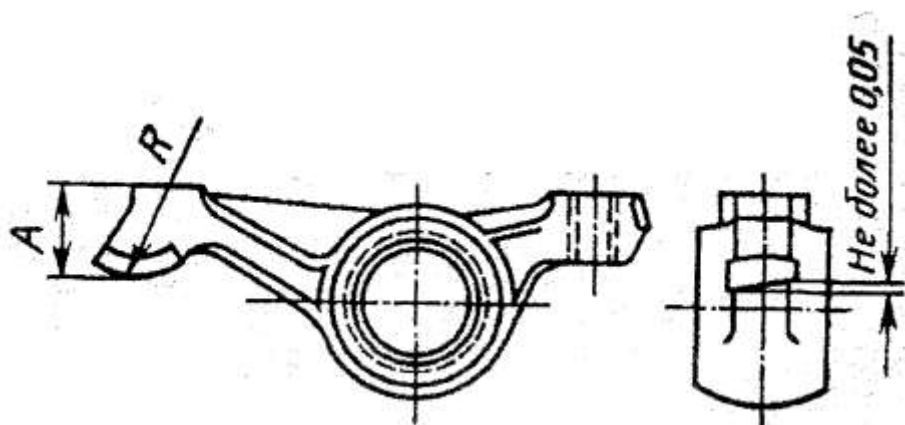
Схема рабочей поверхности бойка коромысла:
